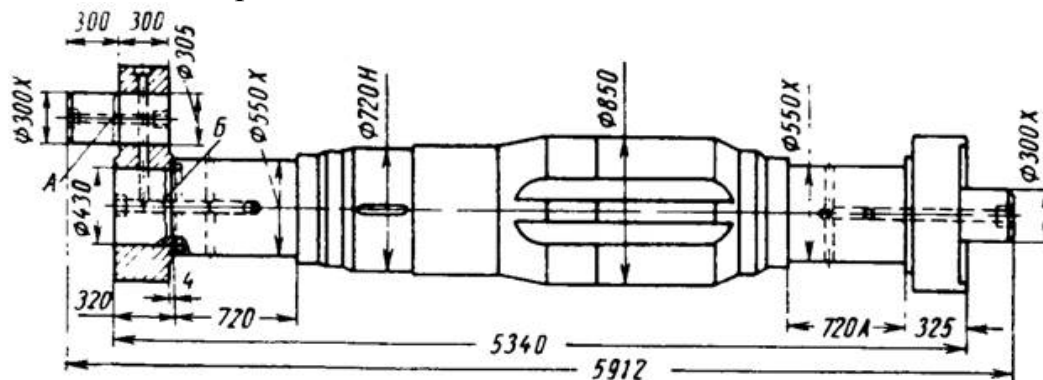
Кривошипный вал компрессора 1Г-266/320
